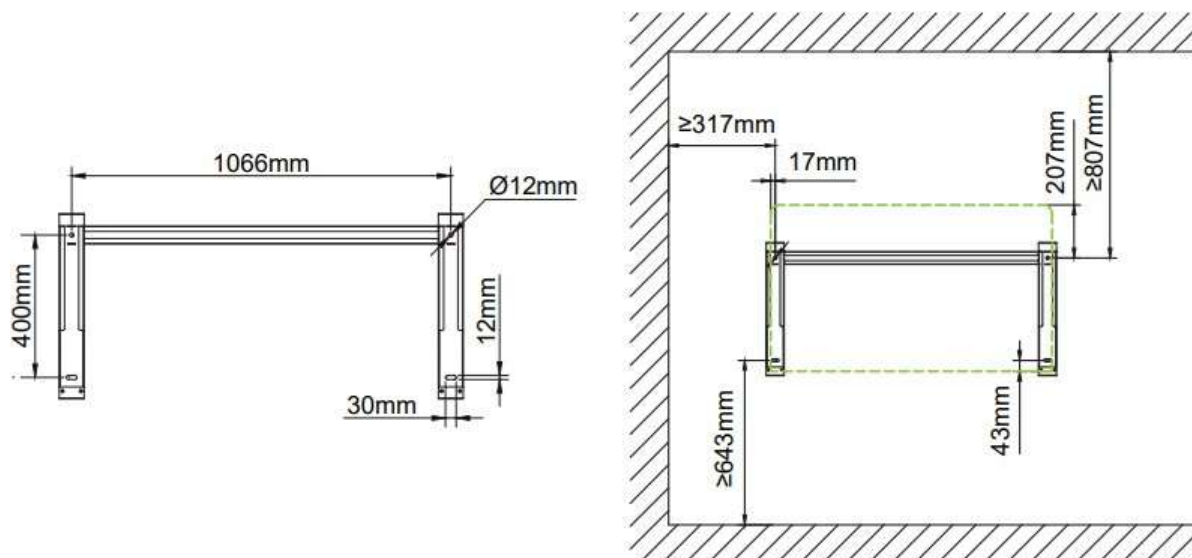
Dimensiones de la posición de los orificios del soporte de montaje
